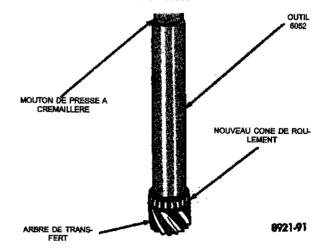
Pose de cône de roulement (0,030 à 0,104 pouce). Si le jeu sort des normes,
